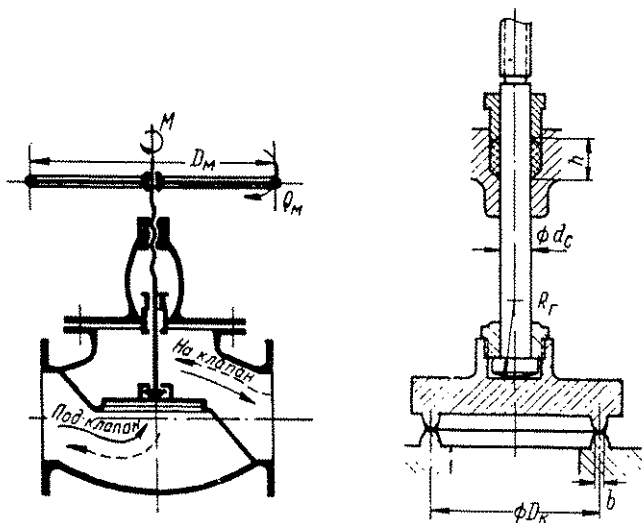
Схема вентиля и конструкция узла шпинделя с тарелкой клапана
